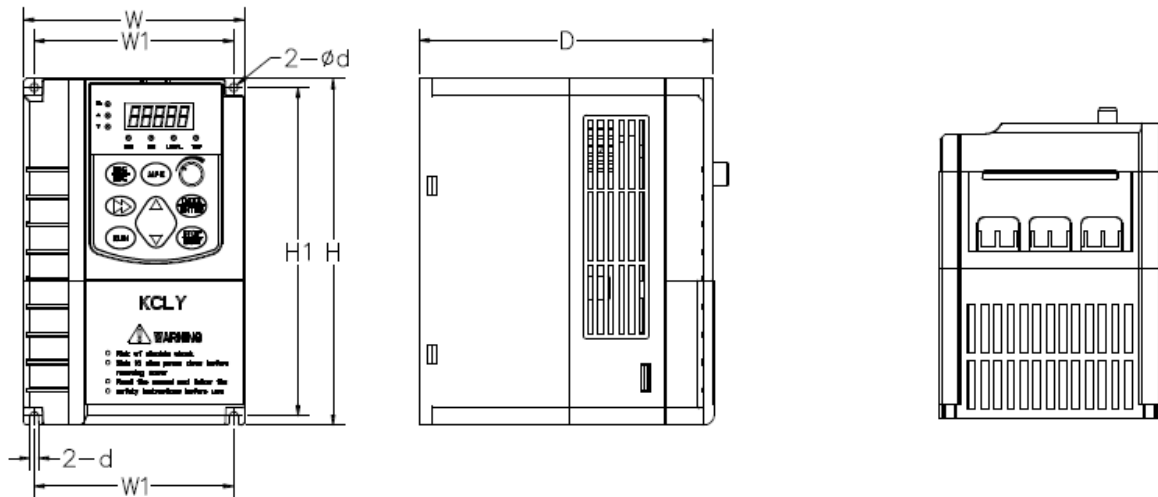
KOC700 系列（带电位器）塑胶结构外形尺寸及安装尺寸示意图
